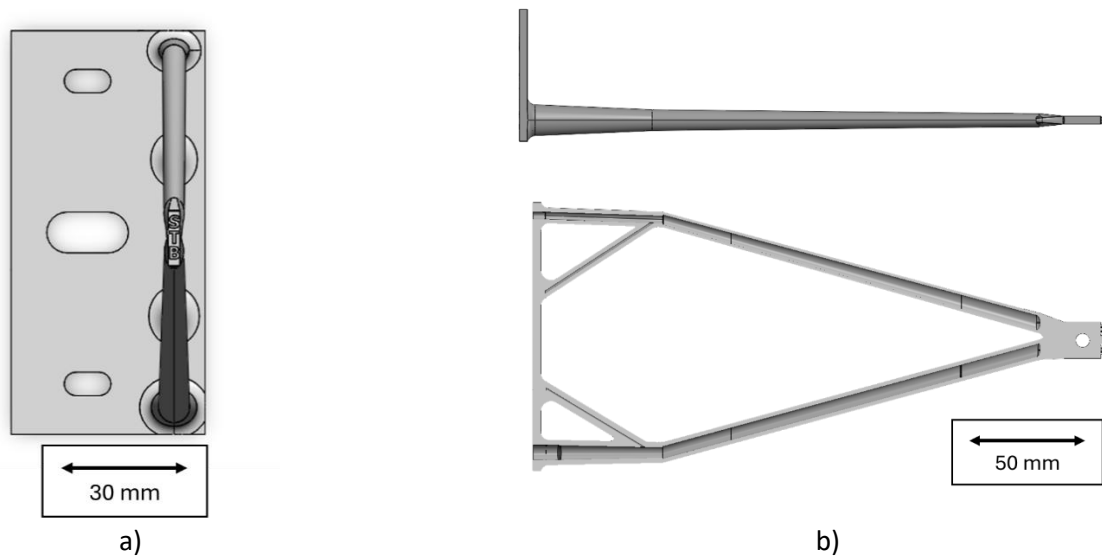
Halter nach der Gewichtete-Summen-Methode für eine Halterlänge von 220 mm a) Draufsicht b) Vorderansicht und Seitenansicht im Schnitt.
